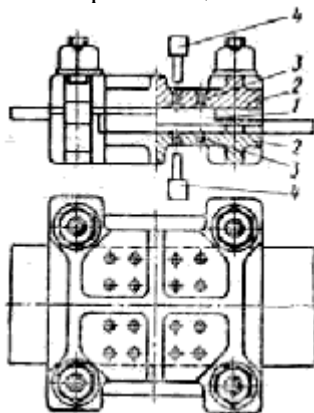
Схема сварки с предварительным зажатием свариваемых деталей в кондукторе: 1 - свариваемые детали, 2 - прижимные плиты, 3 - отверстия, 4 - пуансоны.
